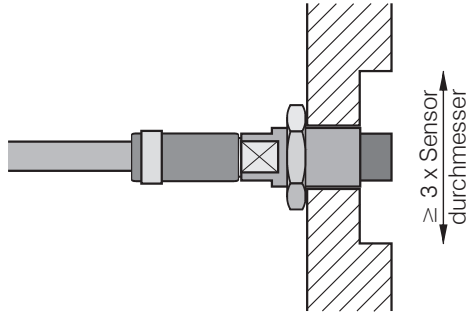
Flächenbündige Montage eines ungeschirmten Sensors in einer metallischen Halterung mit Aussparung
